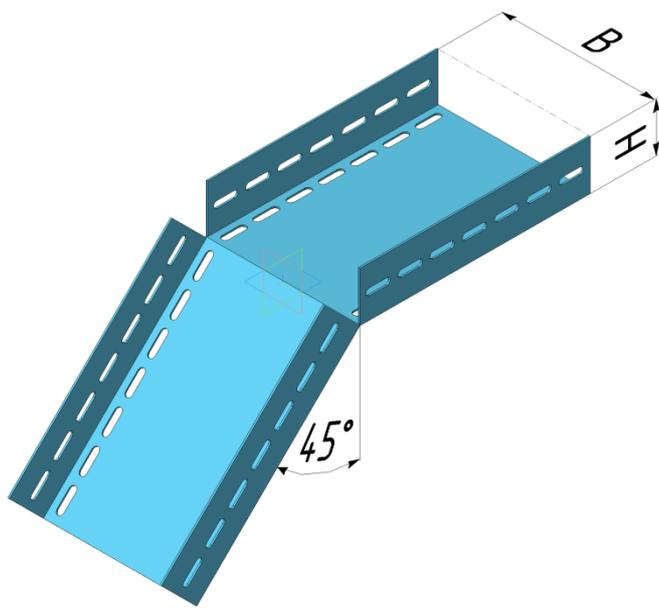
Лоток угловой для поворота трассы вниз под углом 45° типа ЛПН. Общий вид
